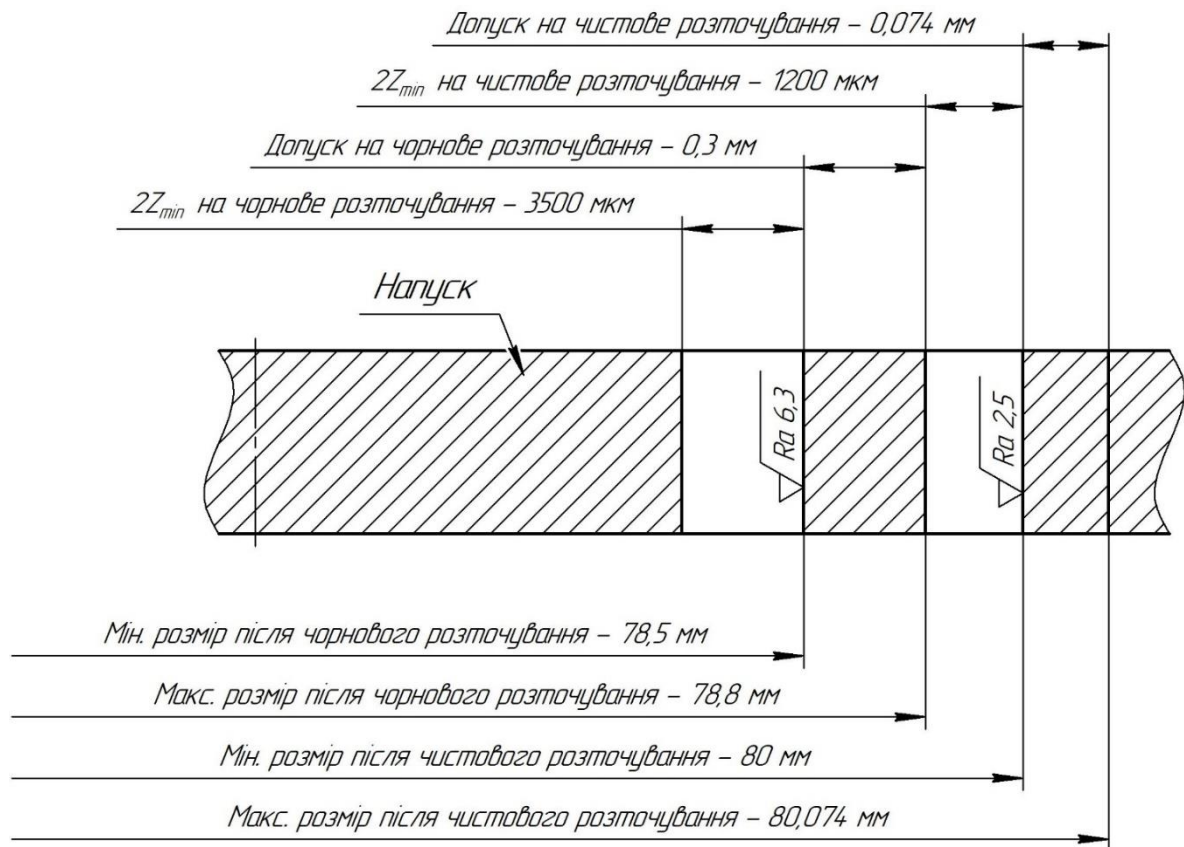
Схема розміщення полів припусків і допусків під час оброблення циліндричного отвору  $\varnothing 85H9$
